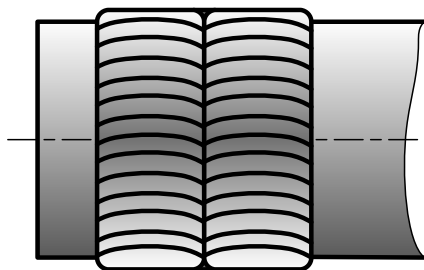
Наплавка тел вращения широкими валиками
